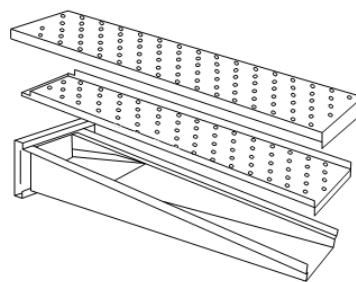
Стандартная верхняя направляющая воздуха.
